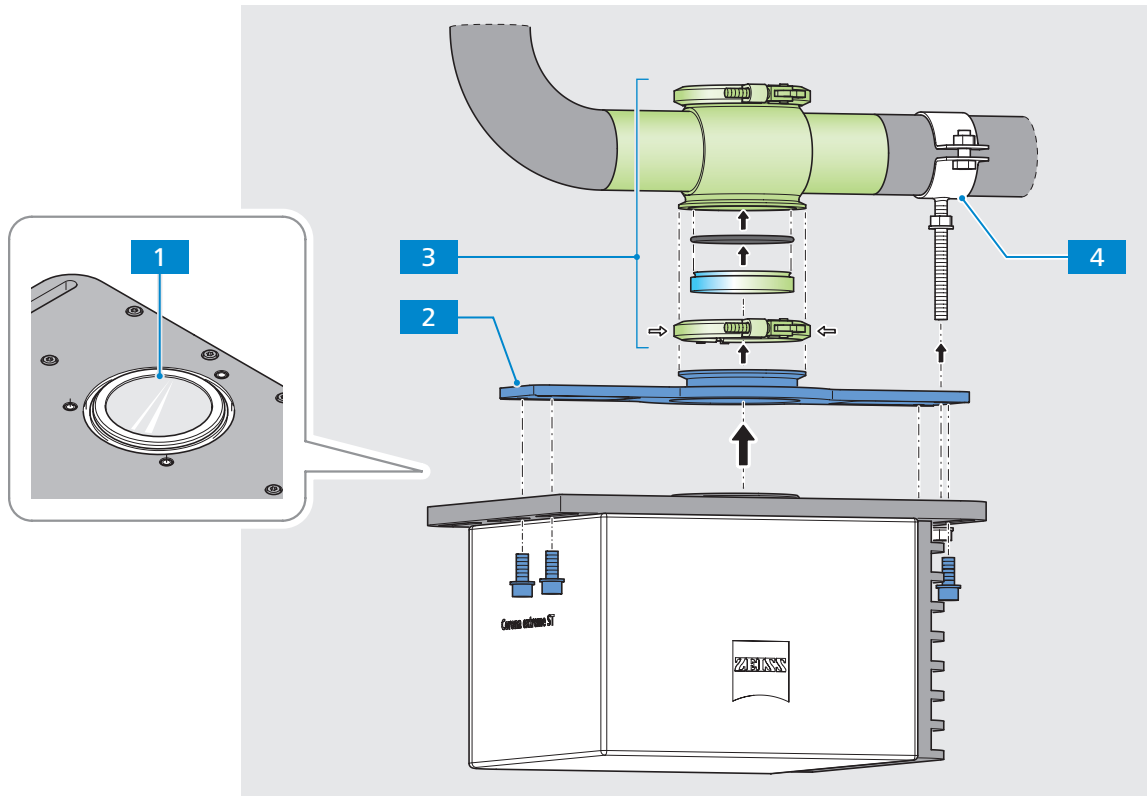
Corona extreme – Montage mit GEA-Flansch
